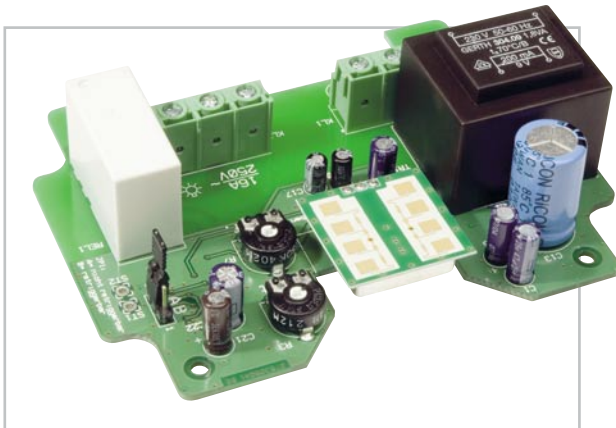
Montage des Sensors zur Erfassung durch den Gehäusedeckel
